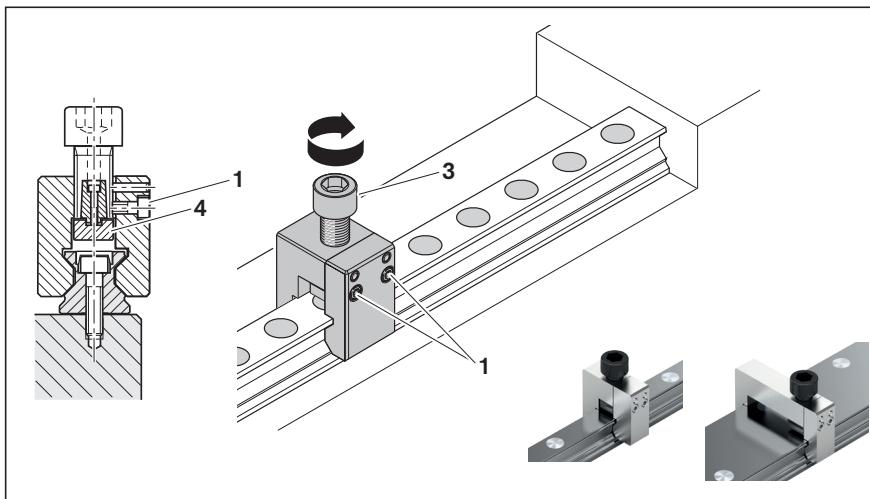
Herramienta de montaje para las cápsulas de protección de acero
